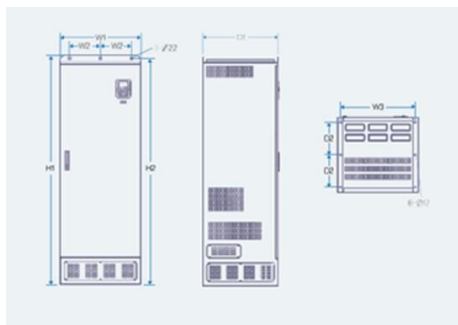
Напольный монтаж ПЧ 355-400 кВт
